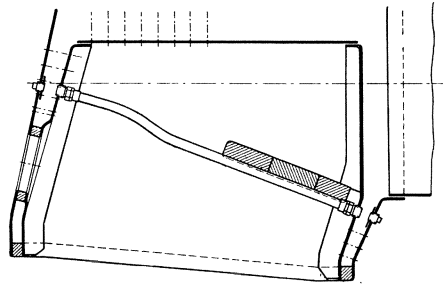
Feuerschirm auf Wasserrohren gelagert (nach Spalckhaver-Rüster).
